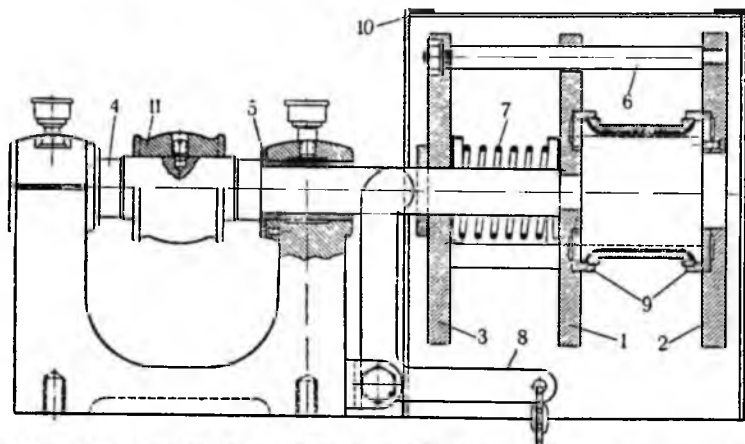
Прибор для центробежной заливки шатунных вкладышей СХТЗ:
